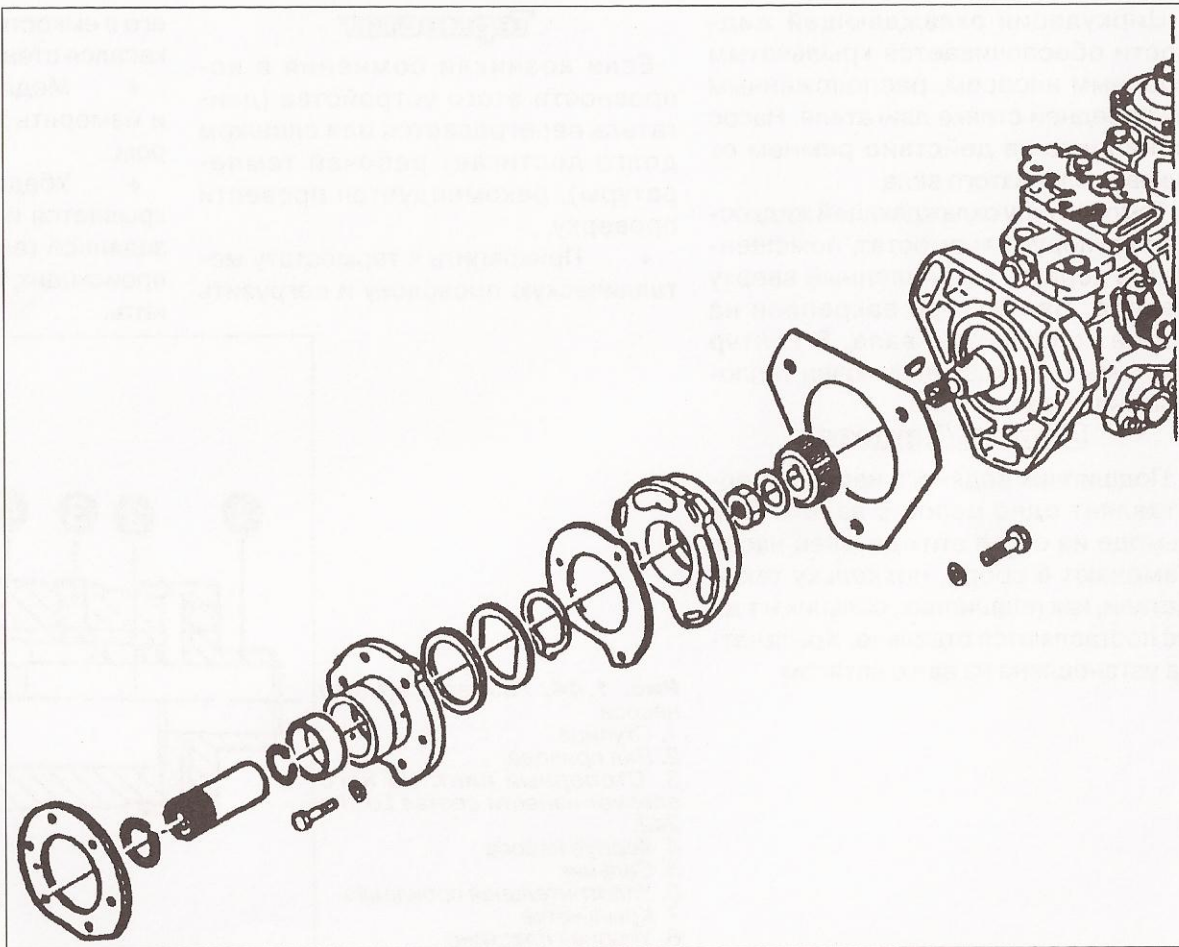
Привод ТНВД (4-цилиндровый и 6-цилиндровый двигатели)
